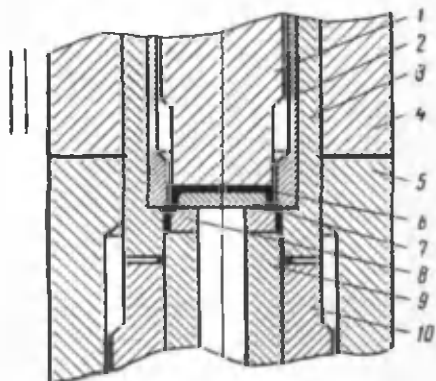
Штамп для изготовления корпусов ртутно-цинковых пуговичных элементов:
